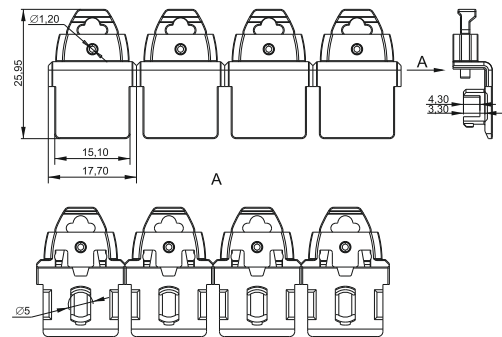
Габаритные размеры заглушки / Figure 2 – Overall dimensions of the plug
